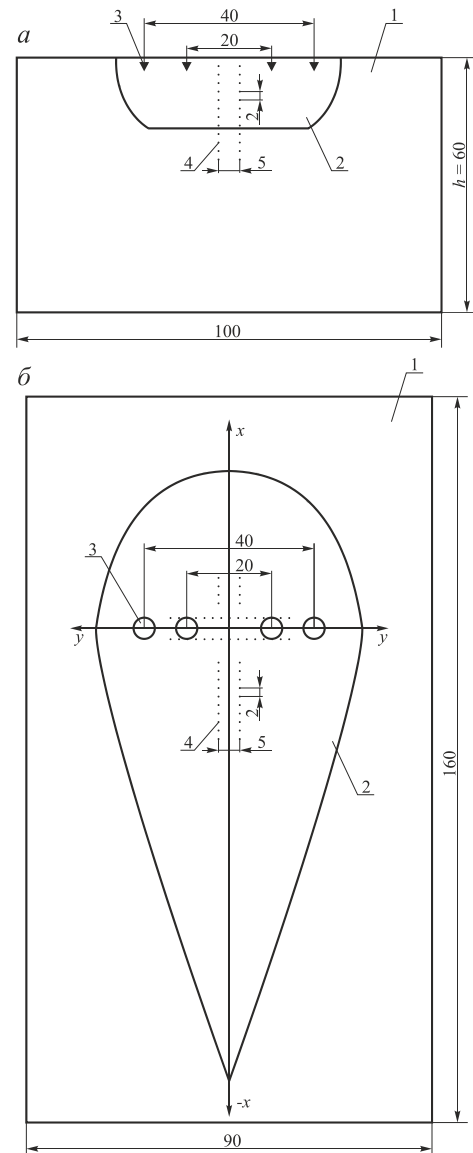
Модели сварочной ванны: а – по глубине ванны; б – по поверхности ванны; 1 – пластина из низкоуглеродистой стали; 2 – пластина из аустенитной немагнитной стали; 3 – токоподводы (электроды); 4 – точки измерения напряжения
